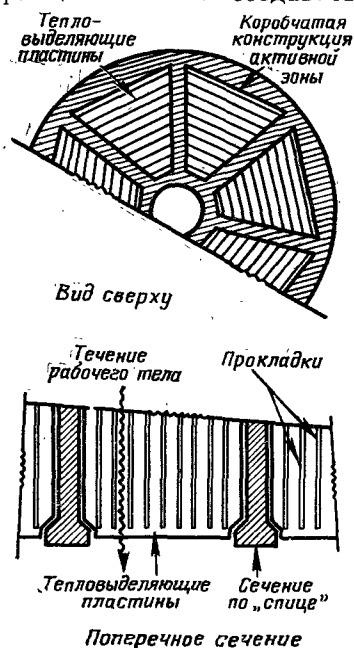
Схема конструкции активной зоны и крепления топливных элементов реактора
